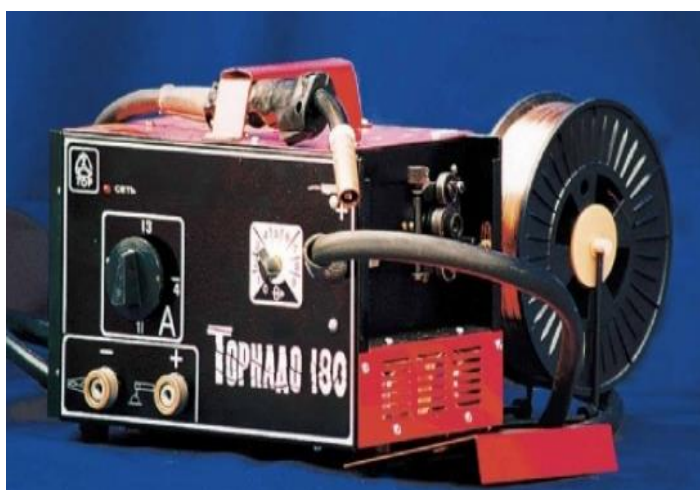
Сварочный полуавтоматический аппарат [17]
